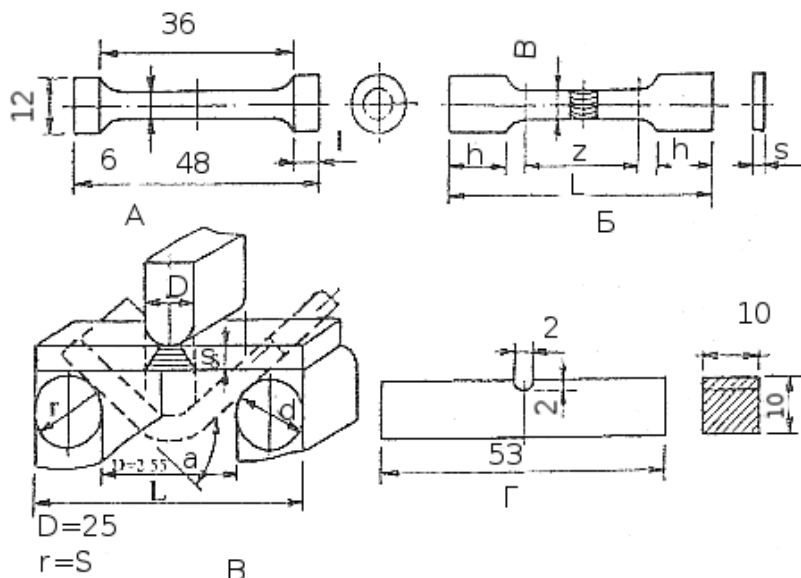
Варианты образцов для определения механических свойств (размеры в мм): А-Б-на растяжение наплавленного металла (А) и сварного соединения(Б); В-на изгиб; Г-на ударную вязкость.
